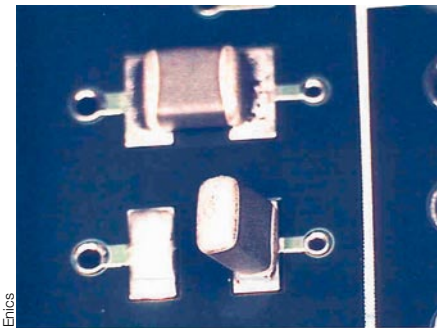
Löttest an 6 Jahre altem Bauelement.
